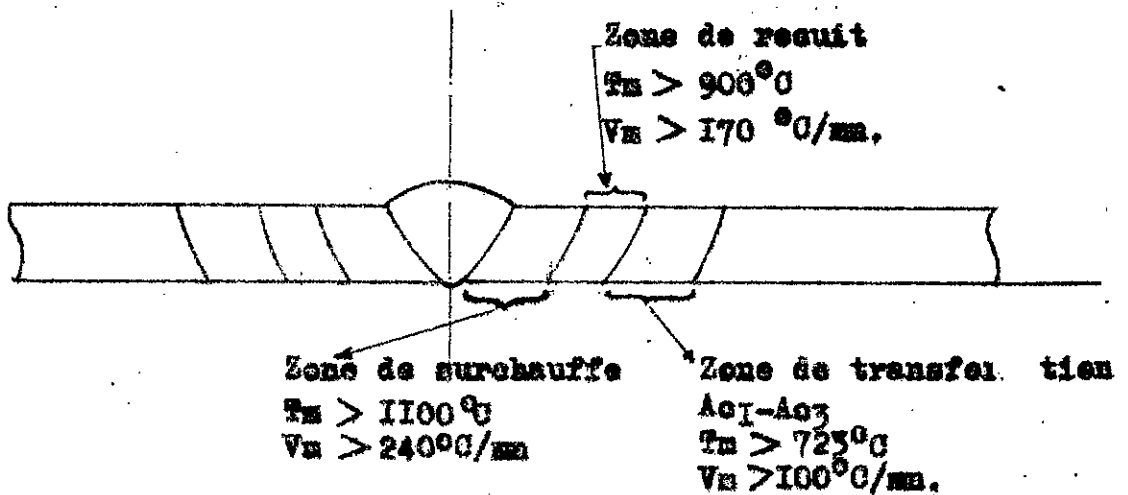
Stat thermique d'un assemblage soudé de deux toles de 10mm d'épaisseur. [3,11]
